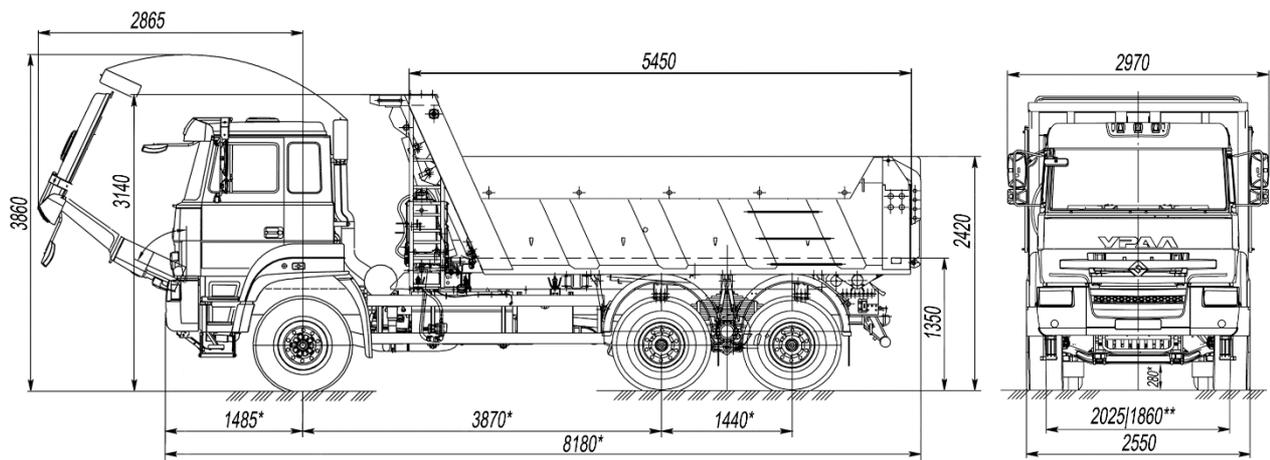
Габаритные размеры автомобиля-самосвала Урал- С34520 (платформа 12 м³)
